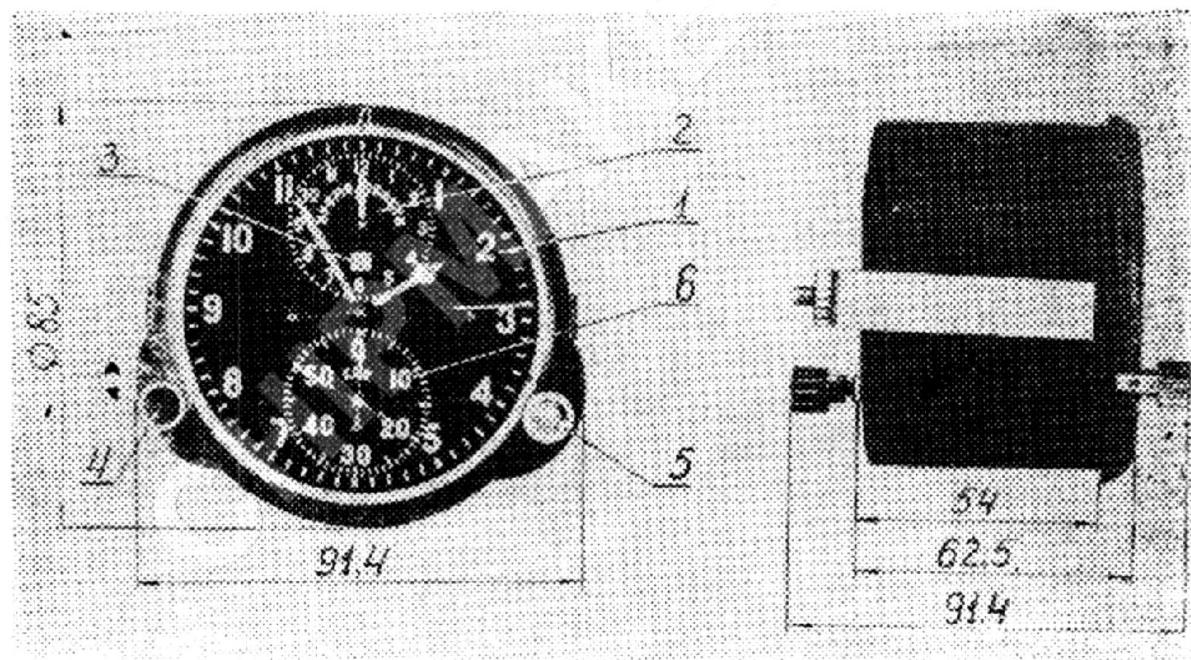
Вид часов АЧС-1 со стороны циферблата и вид сбоку с габаритными размерами:
